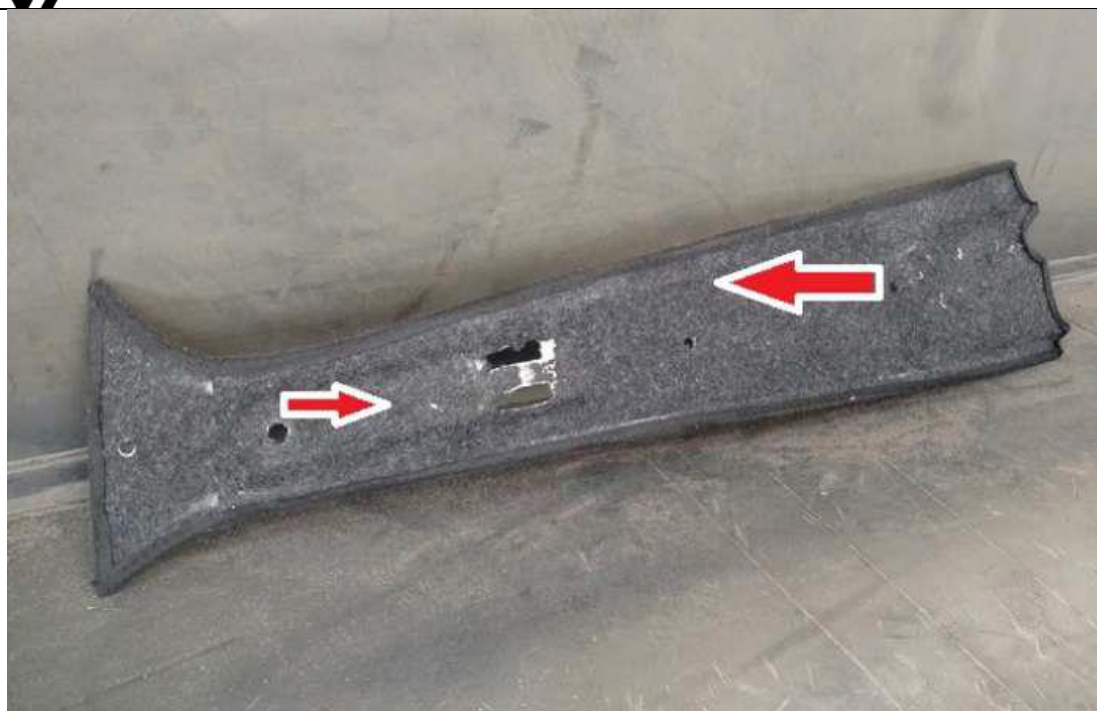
Detalhe do carpete aplicado na face oposta da chapa de aço
